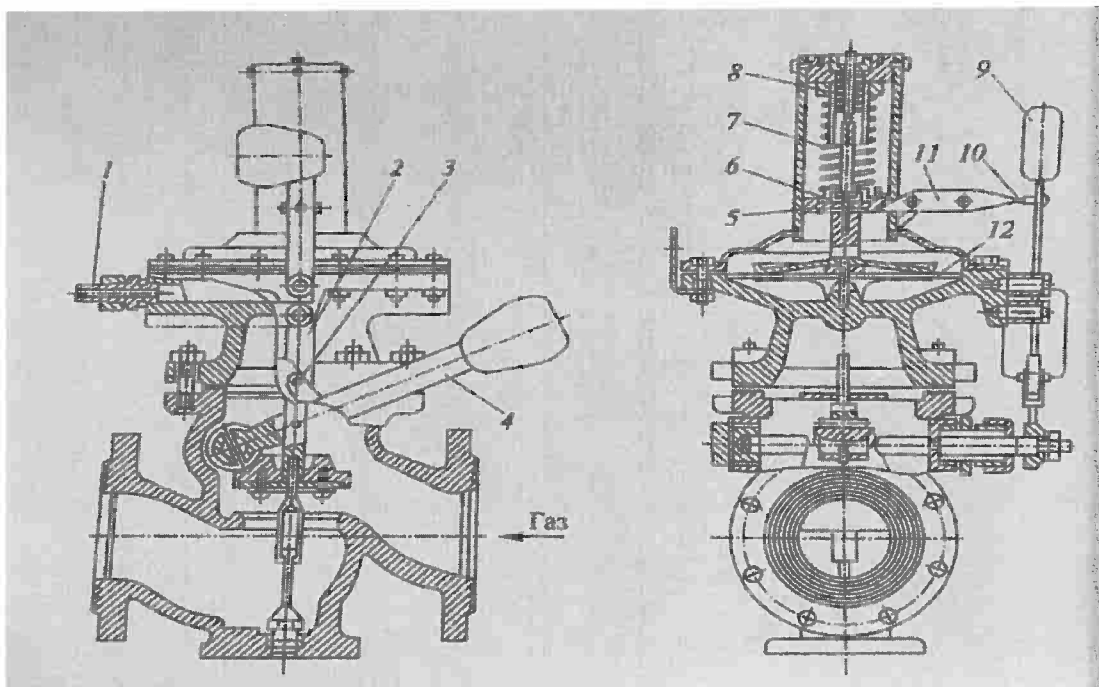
Предохранительно-запорные клапаны ПКН и ККВ: 1-штуцер; 2,4-рычаги; 3,10 - штифты; 5 - гайка; 6 - тарелка; 7,8 - пружины; 9 - ударник; 11 - коромысло; 12 - мембрана.
